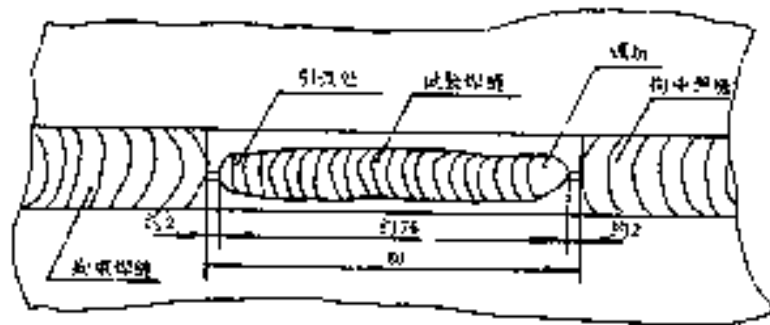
采用焊条自动送进装置焊接试验焊缝位置
